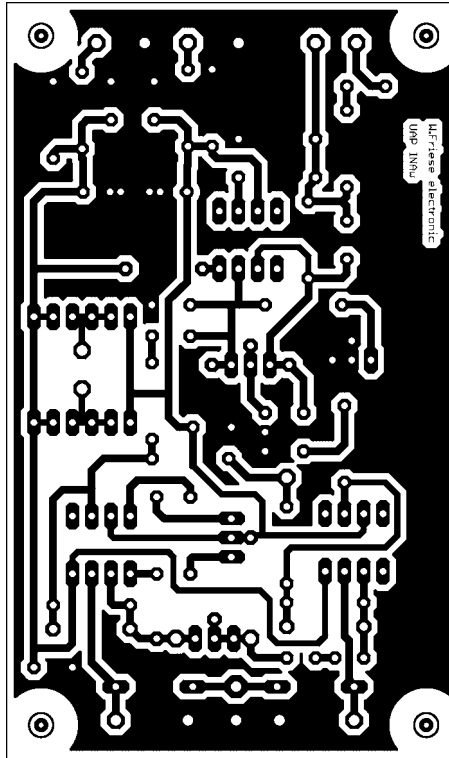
Layout der einseitigen Platine UAP INAw im Maßstab 1:1
